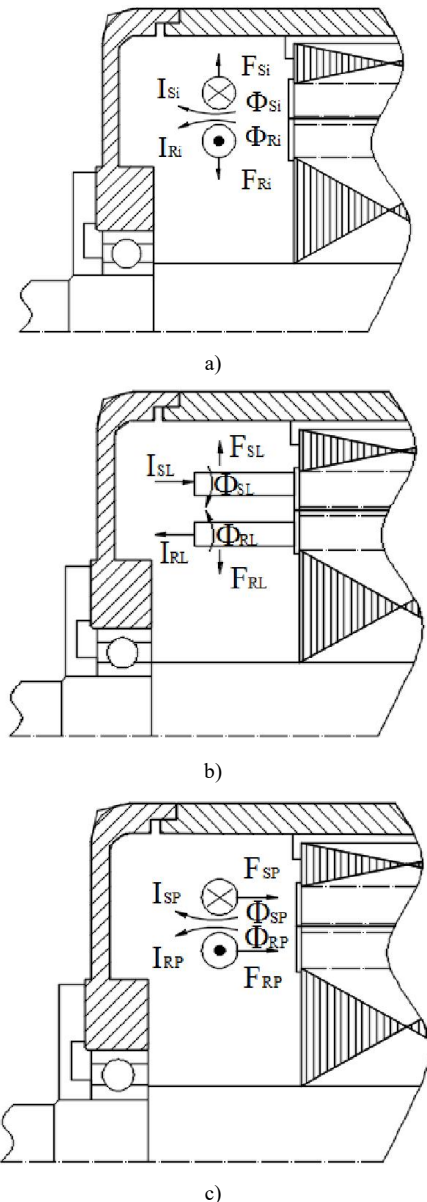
Fragmente de motor asincron cu rotorul bobinat desfășurat în plan.
